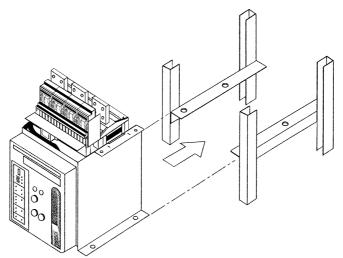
Fixation sur plan horizontal Fijación en plano horizontal
